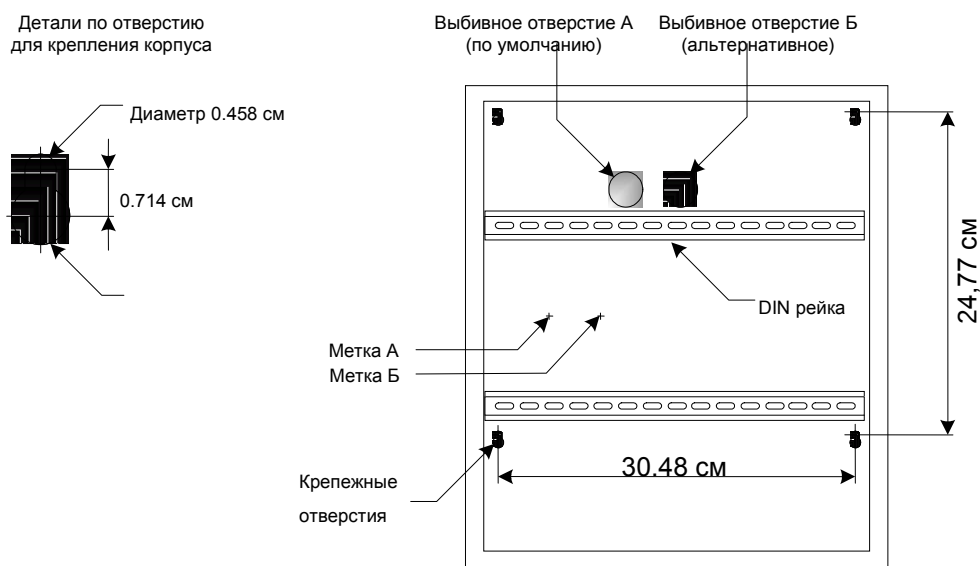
Корпус SCU (показан с DIN рейками и без дверцы)
